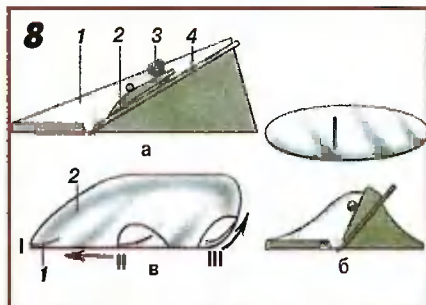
Малогабаритные рубанки: а — «Малютка» (1 — корпус; 2 — прижим; 3 — прижимный винт; 4 — нож); б — для обработки корпусов музыкальных инструментов; в — универсальный (I, II, III — положения ножа при обработке труднодоступных мест, плоских и вогнутых поверхностей соответственно. Стрелками показаны направления строгания: 1 — нож; 2 — корпус).
